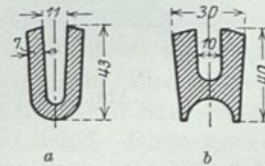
Regelquerschnitte für Aluminium-Schleifstücke; a ohne, b mit durchgehendem Stahlrohr.
